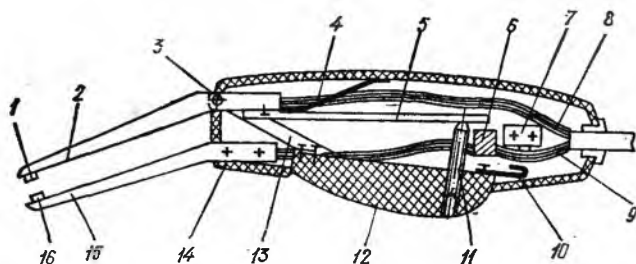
Кинематические схемы пружинного механизма сжатия с ручным приводом для сварки в монтажных условиях (клещи).
